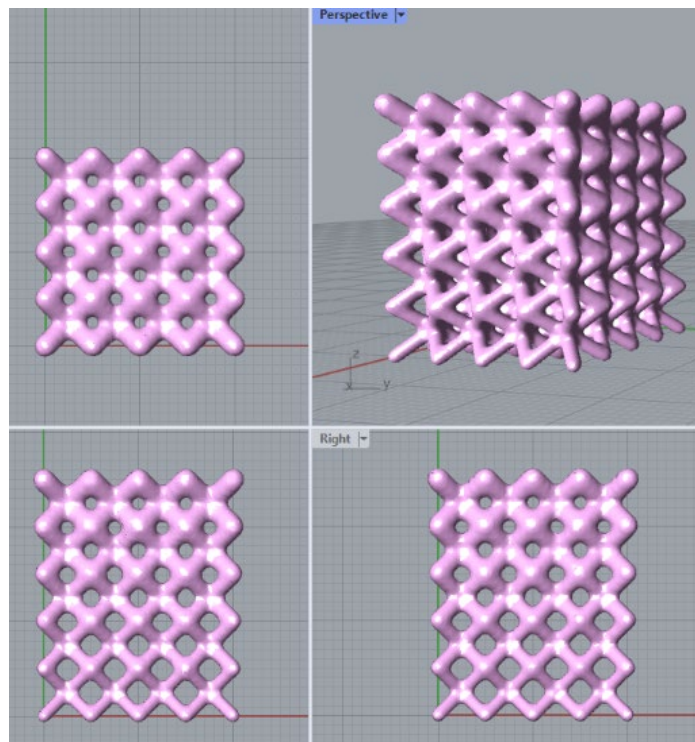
Viste della struttura reticolare cubica a corpo centrato con gradiente tramite distanza da un piano attrattore
